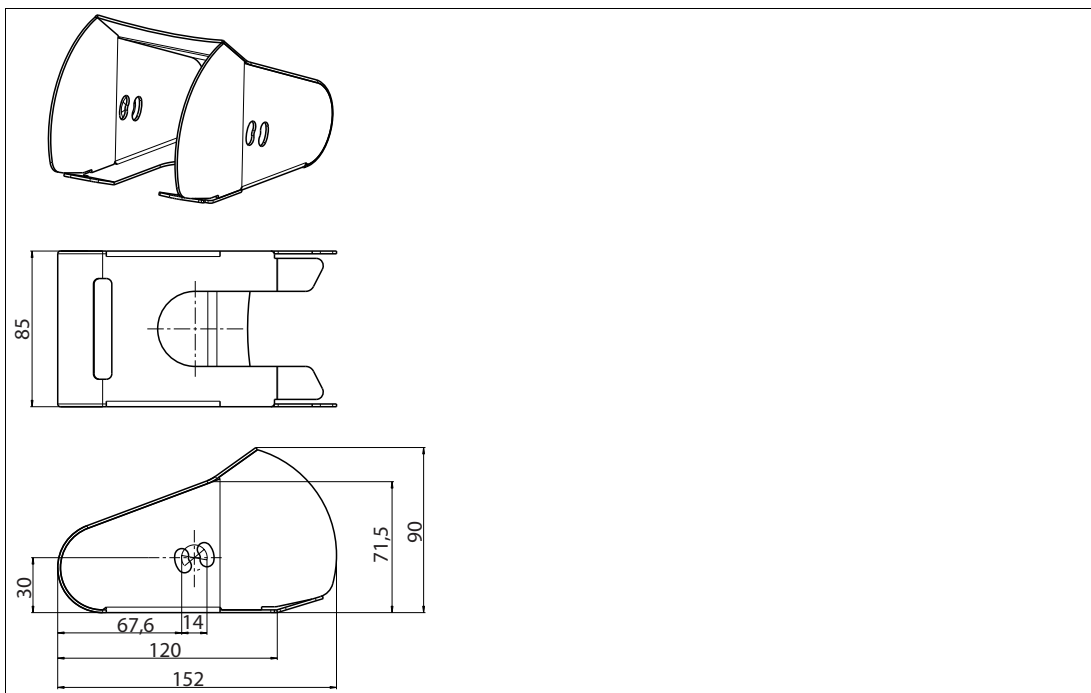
Abmessungen Halter für Barcode-Handheld
